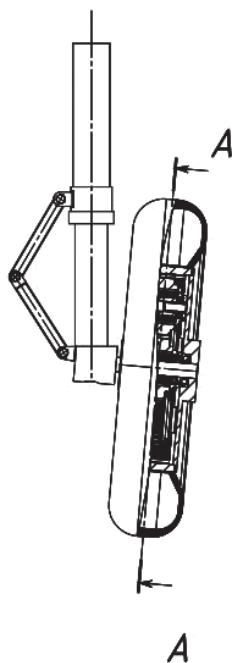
Схема расположения редуктора в колесе шасси (пример)
